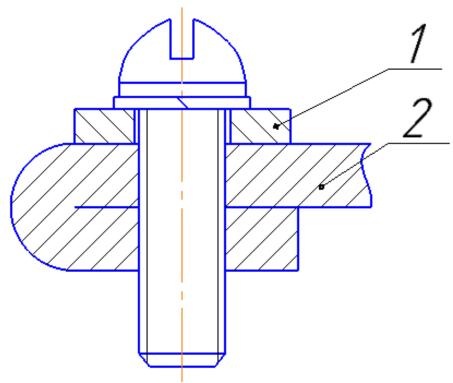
Увеличение длины резьбового отверстия за счет гибки листа: 1 – накладка; 2 – заготовка.
